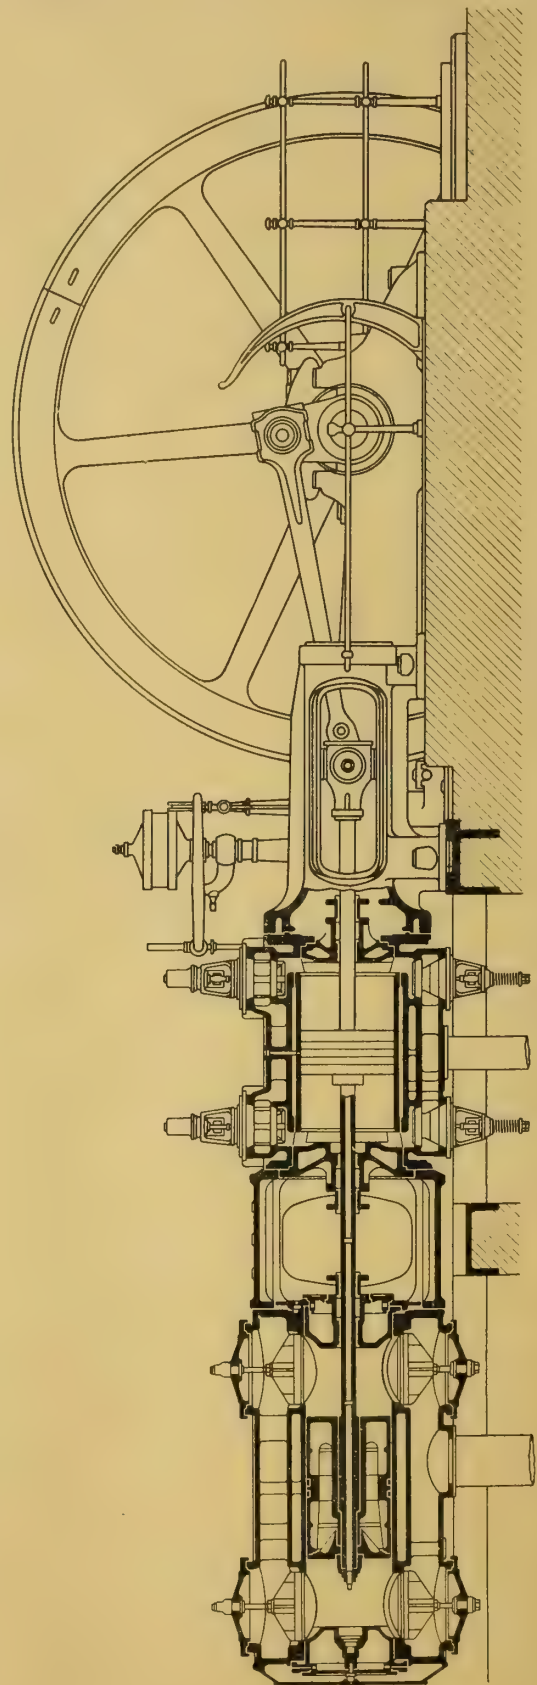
Kompressor von R. Meyer, Mülheim-Ruhr.
